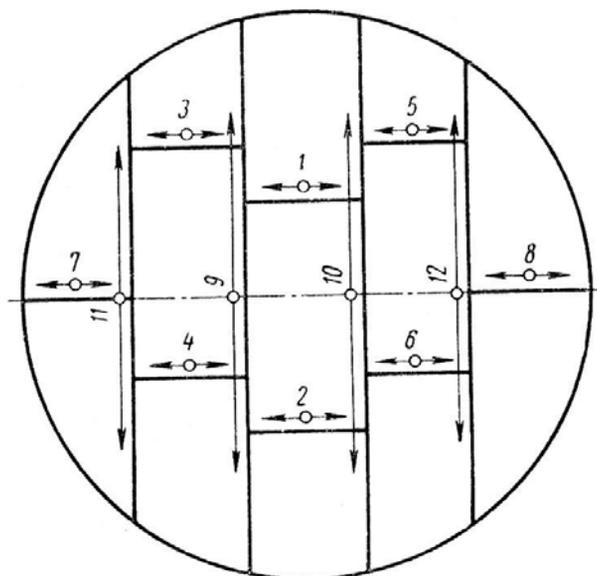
Сварка крупногабаритных плоских днищ
